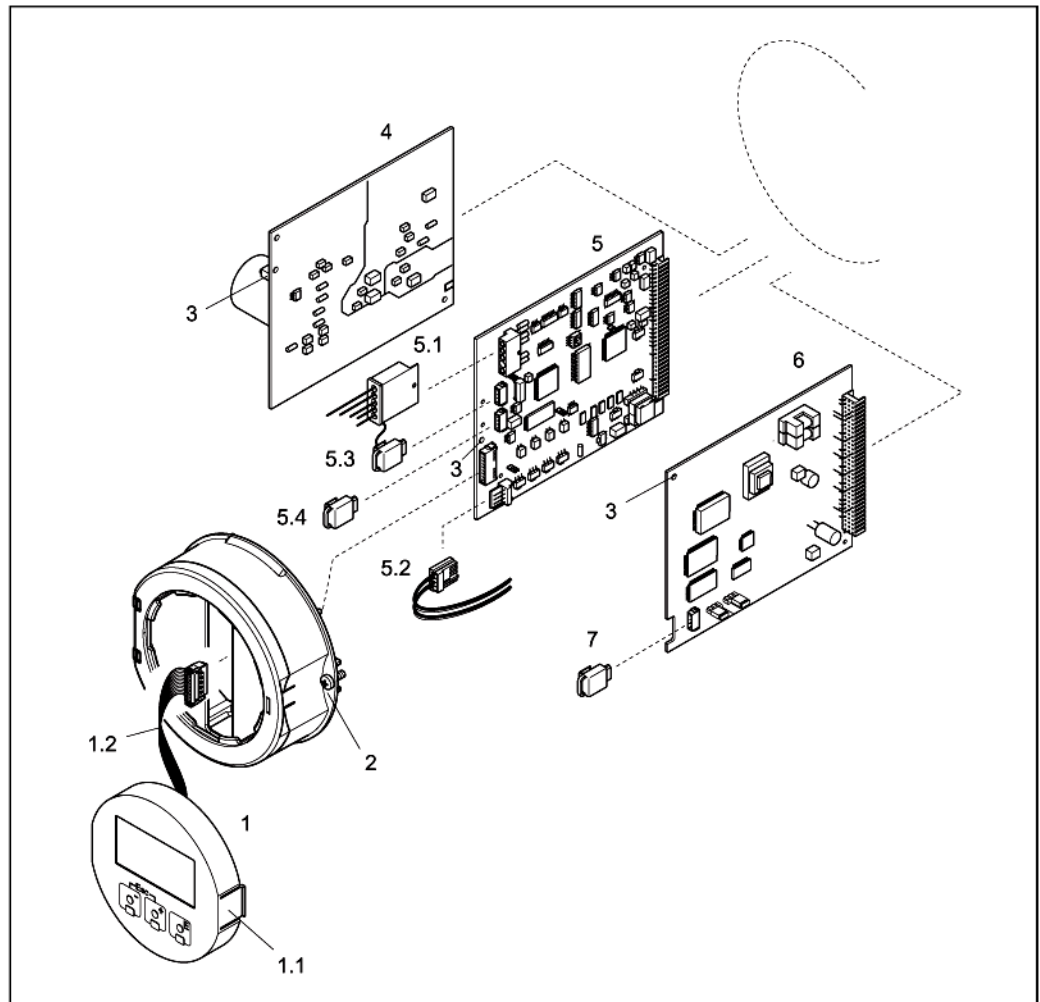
Полевой корпус: установка и удаление плат электронного модуля
